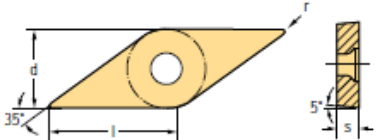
Vybraný soustružnický nůž pro hrubování.
